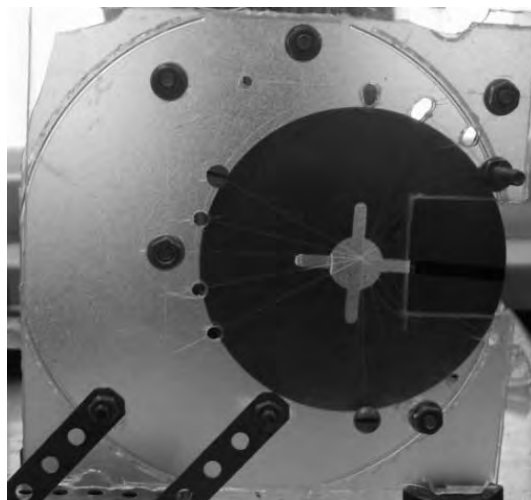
Фотография общего вида кассеты для бесцентрового шаржирования диска
